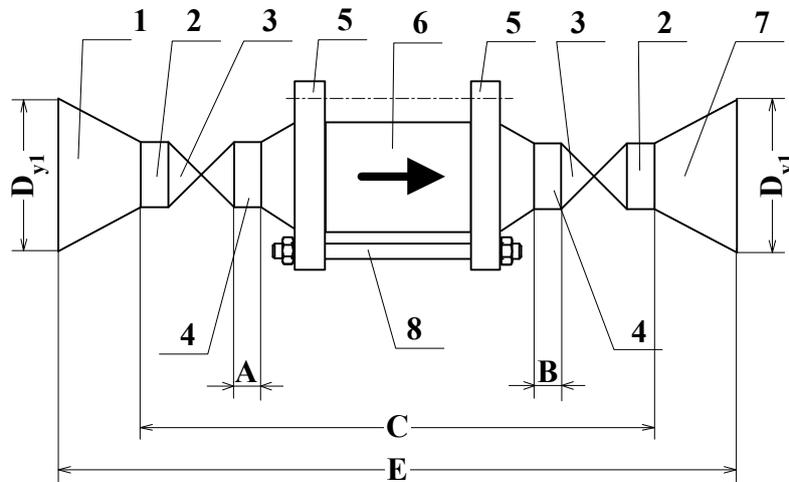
Схематическое изображение сборочно-сварной конструкции с шаровыми задвижками для установки ППРЭ в трубопровод
